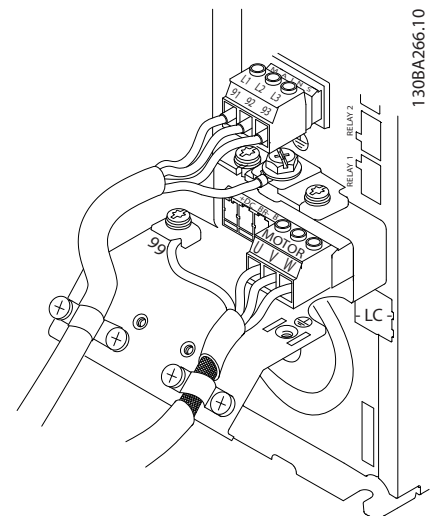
Befestigung der Zugentlastungsklemme
